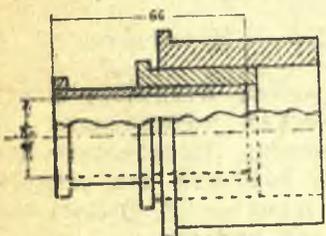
Сборная втулка для крепления заготовки  $\varnothing 26,6$  мм при дальнейшей обточке и нарезке
